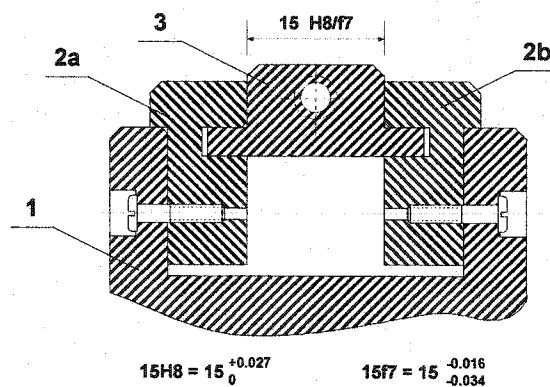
Sous-ensemble de glissière. 1 – corps, 2a et 2b – glissières rapportées, 3 – traînard [CHEV-88]
